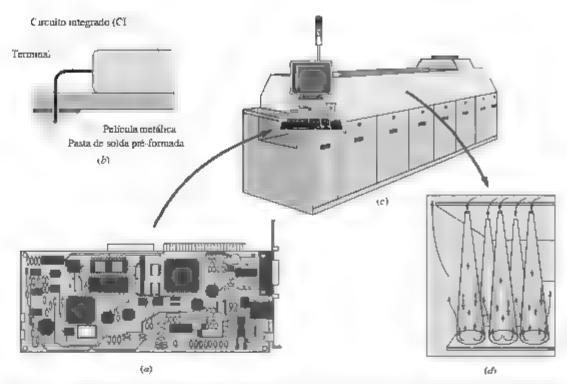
As placas de circuito impresso a serem soldadas (a) com pasta de solda pré-formada aplicada aos pinos dos circuitos integrados (b) entram no forno de soldagem por refluxo (c) em um transportador e são aquecidas à tem peratura de fusão da souda por jatos de ar quente condentes (d).
